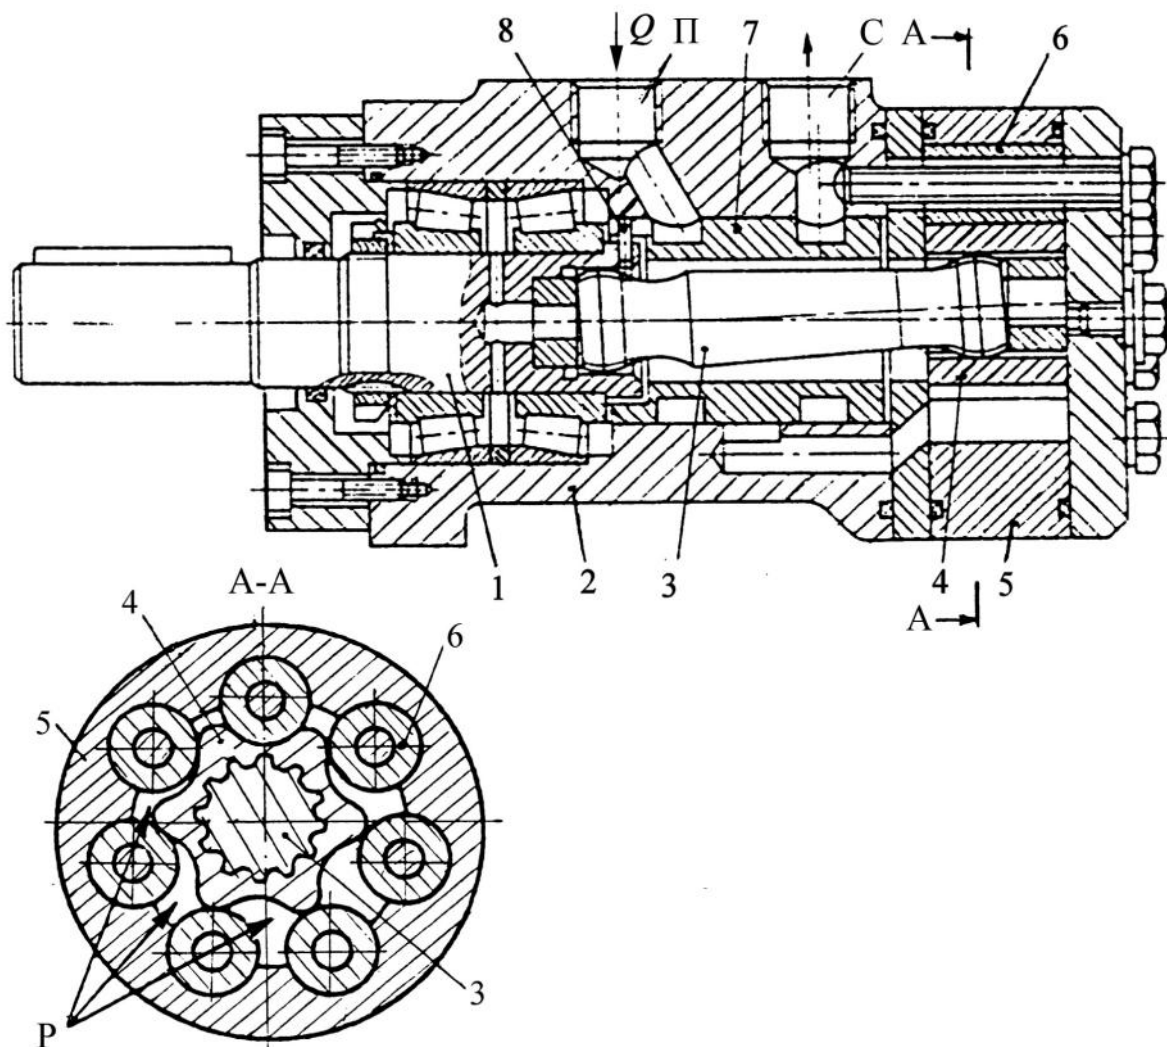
Устройство орбитального гидромотора: 1 – выходной вал; 2 – корпус; 3 – промежуточный вал; 4 – ротор; 5 – обойма; 6 – ролик; 7 – распределительная втулка; 8 – штифт
